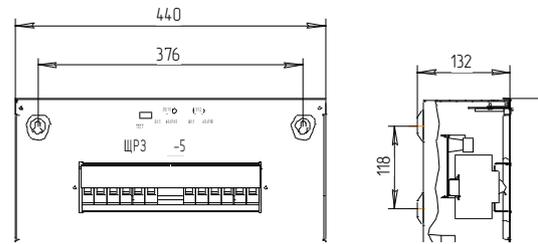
Габаритный чертеж ЩРЗ-5-2
